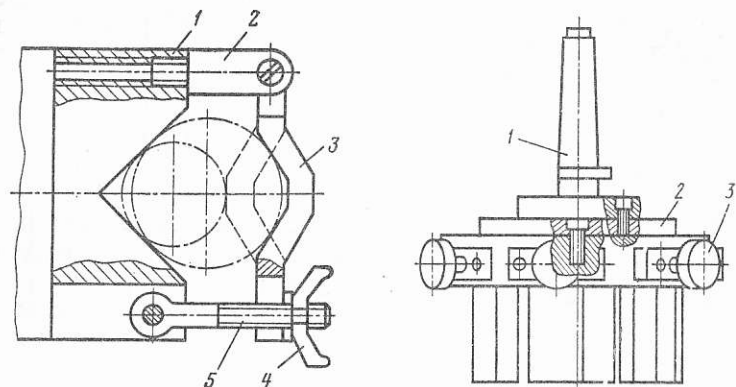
Универсальное приспособление для установки заготовки переменного сечения
